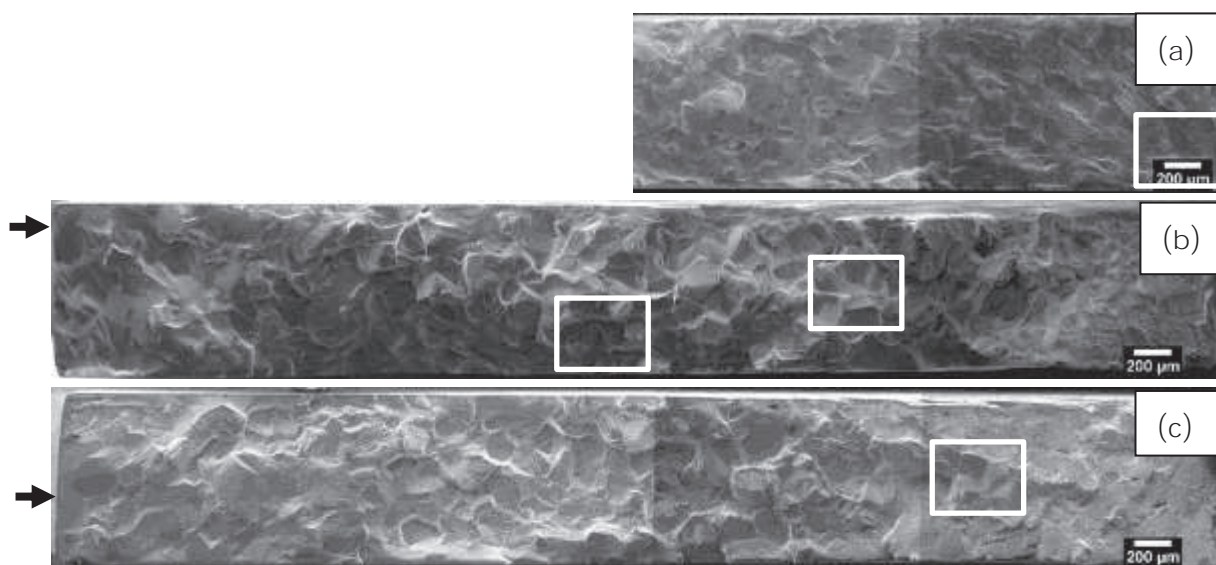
Faciès de rupture des éprouvettes rompues en fatigue à 550°C, éprouvette non vieillie (a) et éprouvettes vieillies pendant 500h à 450°C (b) et 600°C (c)
